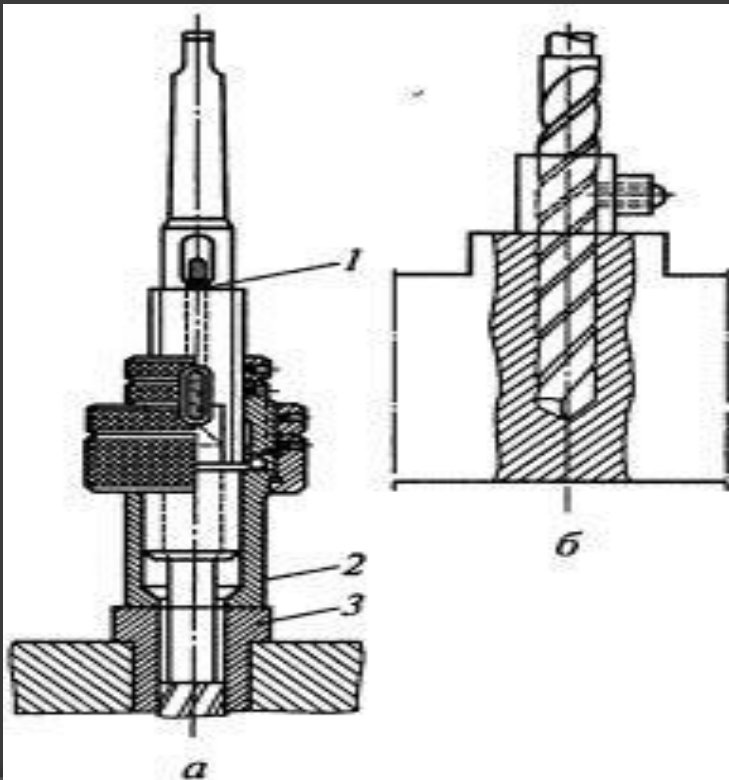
Приспособление для ограничения движения подачи шпинделя:
